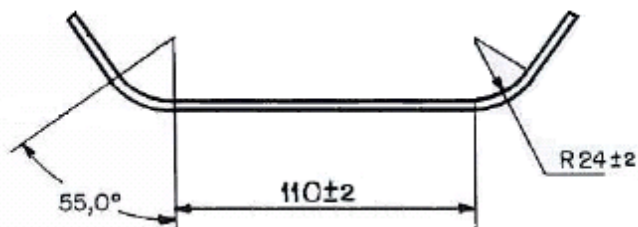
Suporte para fixação do LDS (dimensões em mm)
